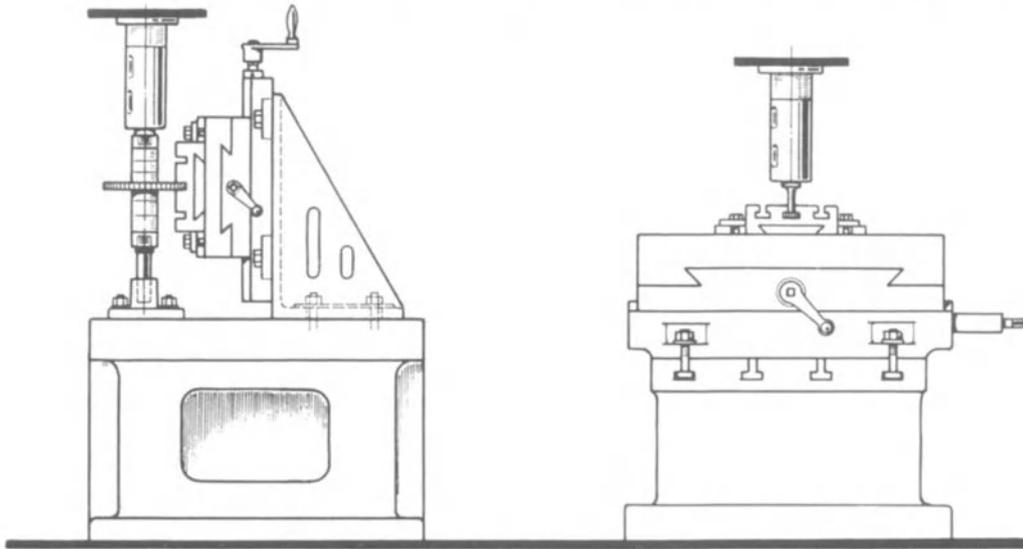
Beispiel für das Fräsen mit der Radialbohrmaschine
